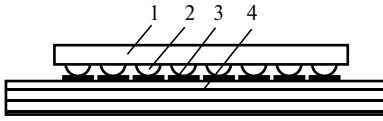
Монтаж микросхемы на подложку методом перевернутого кристалла: 1 — кристалл микросхемы, 2 — шариковый вывод, 3 — контактная площадка монтажной подложки, 4 — монтажная подложка (печатная плата)
